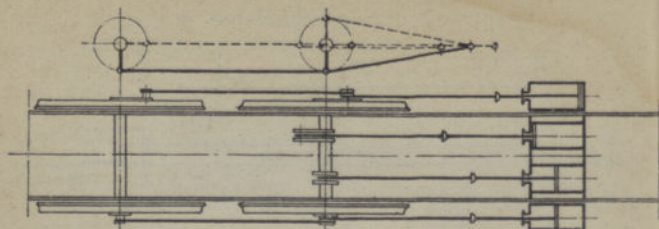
Mechanismo motor de simples expansão, de 4 cilindros.
